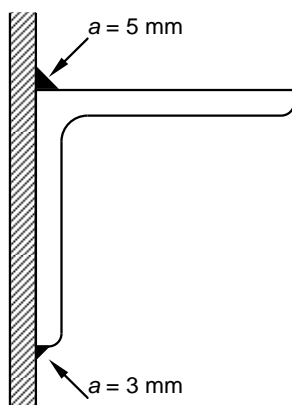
Espesor de garganta de los cordones de soldadura
